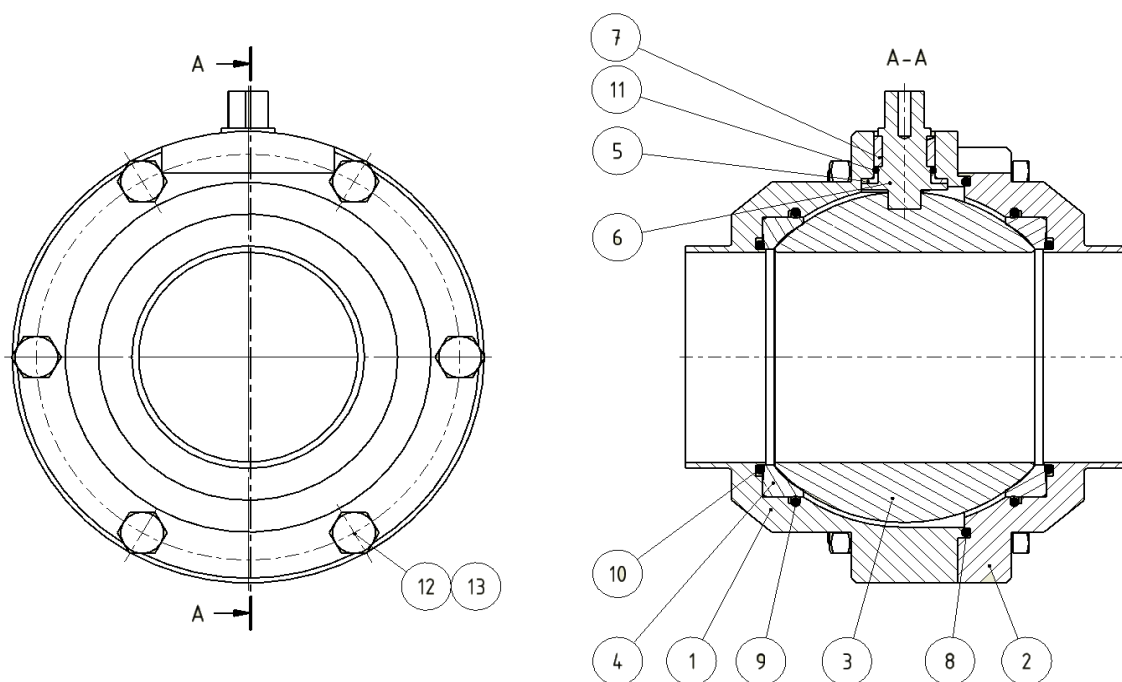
Schnittzeichnung Kugelventil-SS ohne Betätigung (Schweißausführung)
